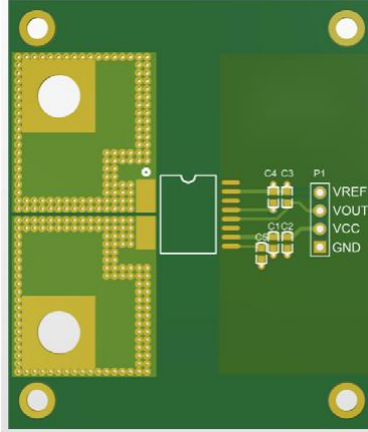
PCB 布局图 (尺寸单位: mm) /Figure 16 PCB layout (size unit: mm)
